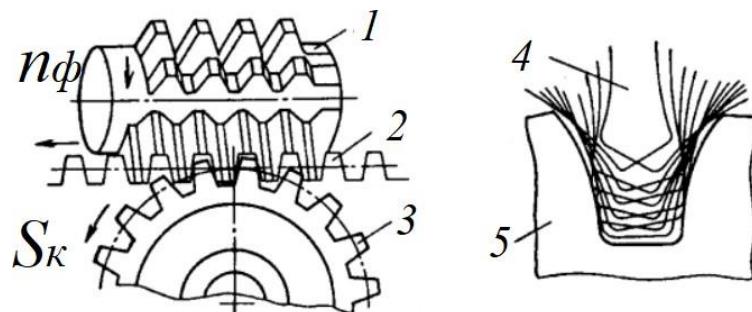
Схема нарізування прямозубого колеса [34]
